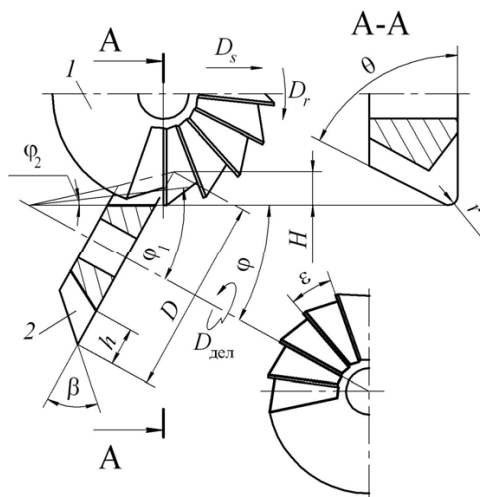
Установка заготовки при фрезеровании конической поверхности:
